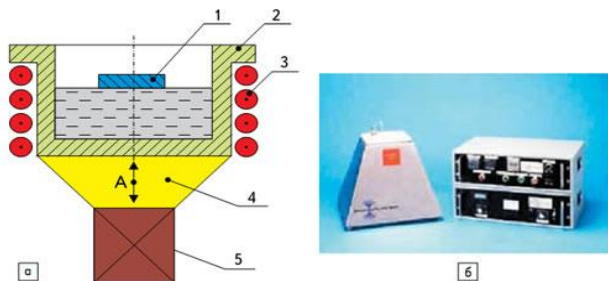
УЗ-ванна с возбуждением всей массы припоя: а) схема: 1 — паяемая деталь; 2 — ванна; 3 — нагреватель; 4 — излучатель; 5 — преобразователь; б) общий вид
